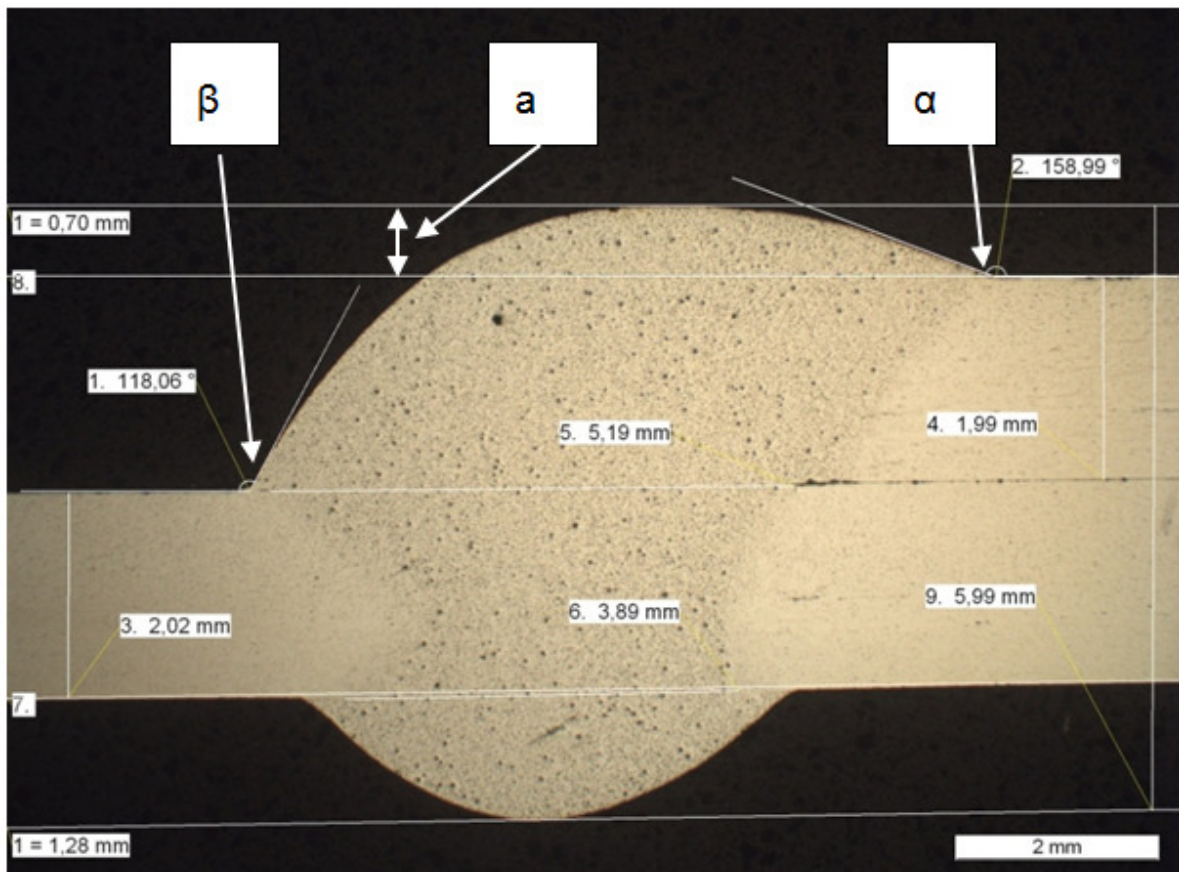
Querschliff - Probe 29 (Schweißzusatz AM50A)
